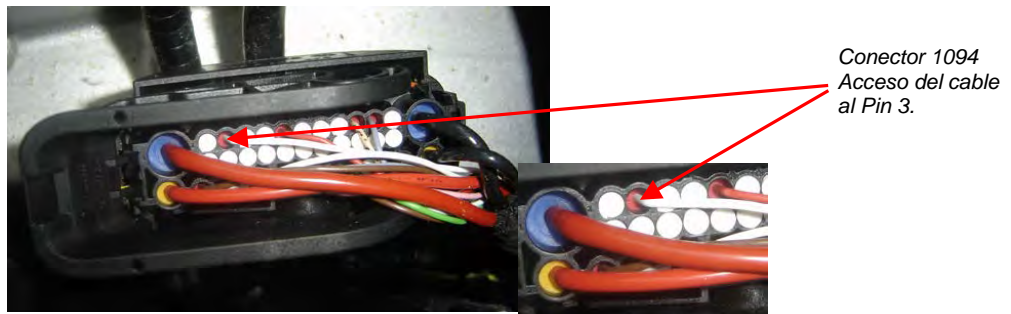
Vista del acceso de cables al conector (parte posterior). El cable verde de señal irá soldado en esta parte, en el pin 3.
